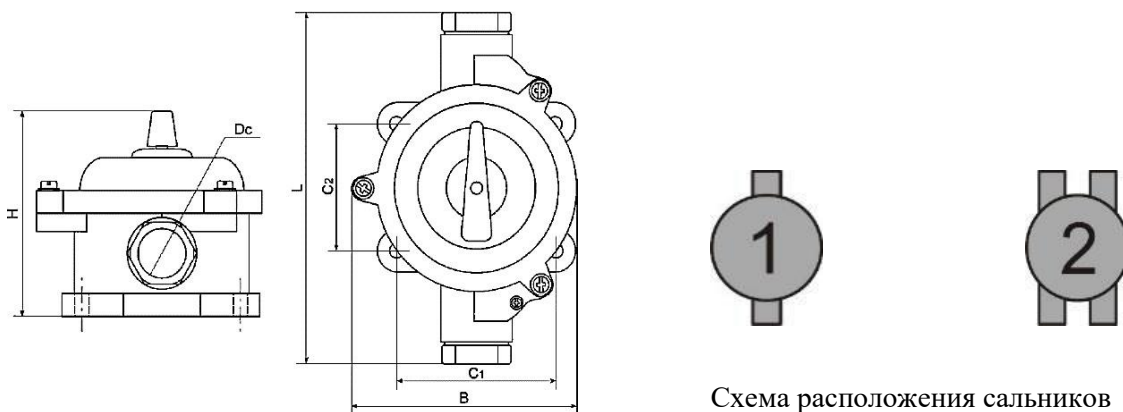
Габаритные и установочные размеры пакетных выключателей ПВ. Исполнение в силуминовом корпусе. Степень защиты IP56. Способ крепления – основанием корпуса.
